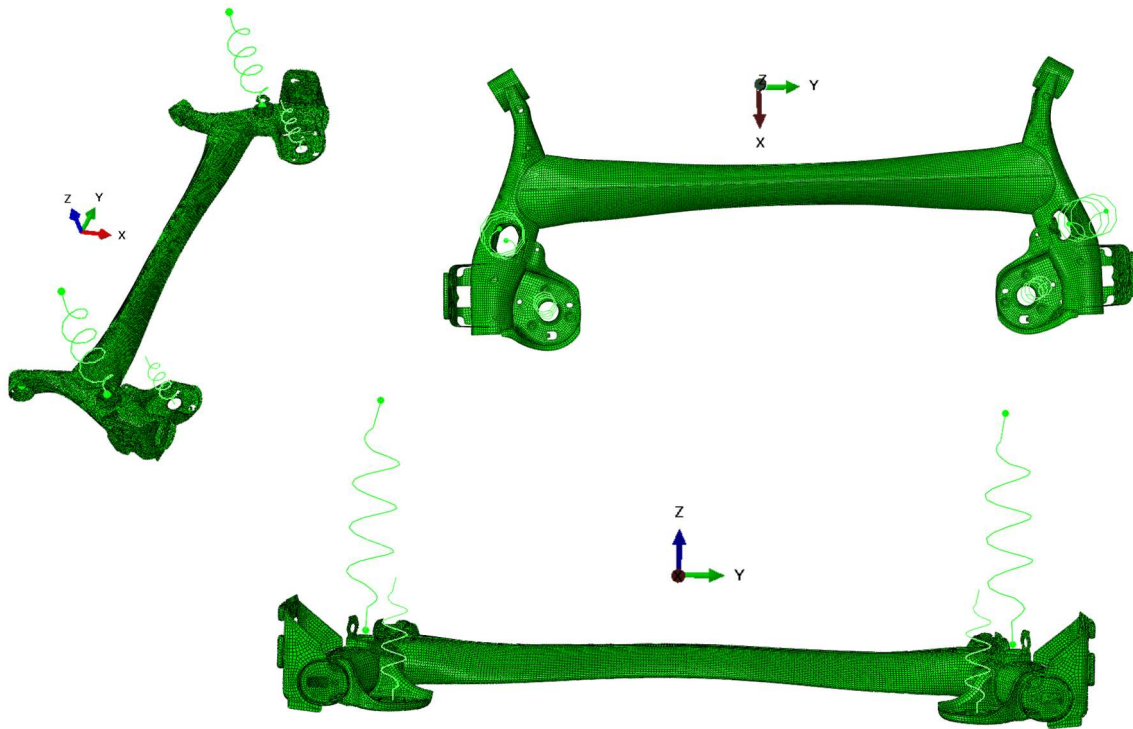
Modèle de la traverse arrière déformable, a) vue plongeante, b) vue de haut, c) vue de derrière le véhicule
